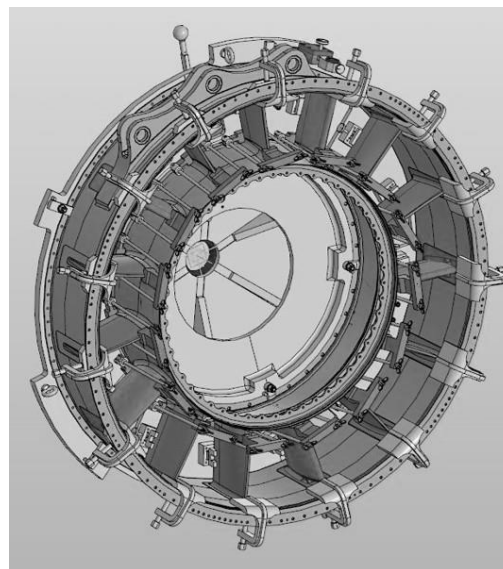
Сборочно-сварочное приспособление с корпусом опоры ТНД
